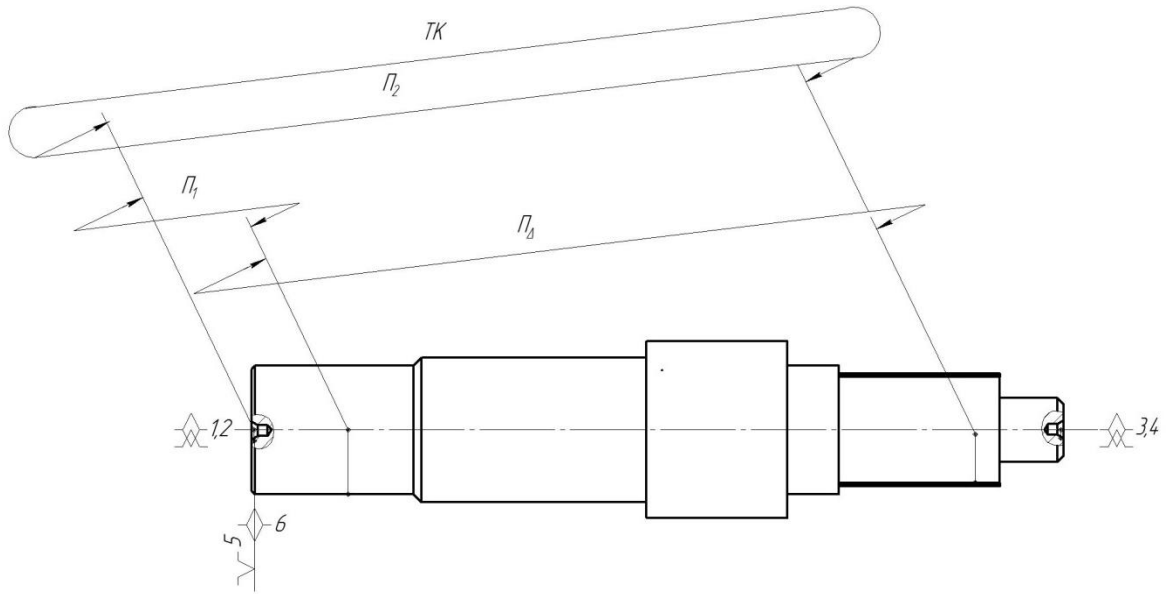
Базування вала (другий варіант) при обробці поверхні під шестерню
